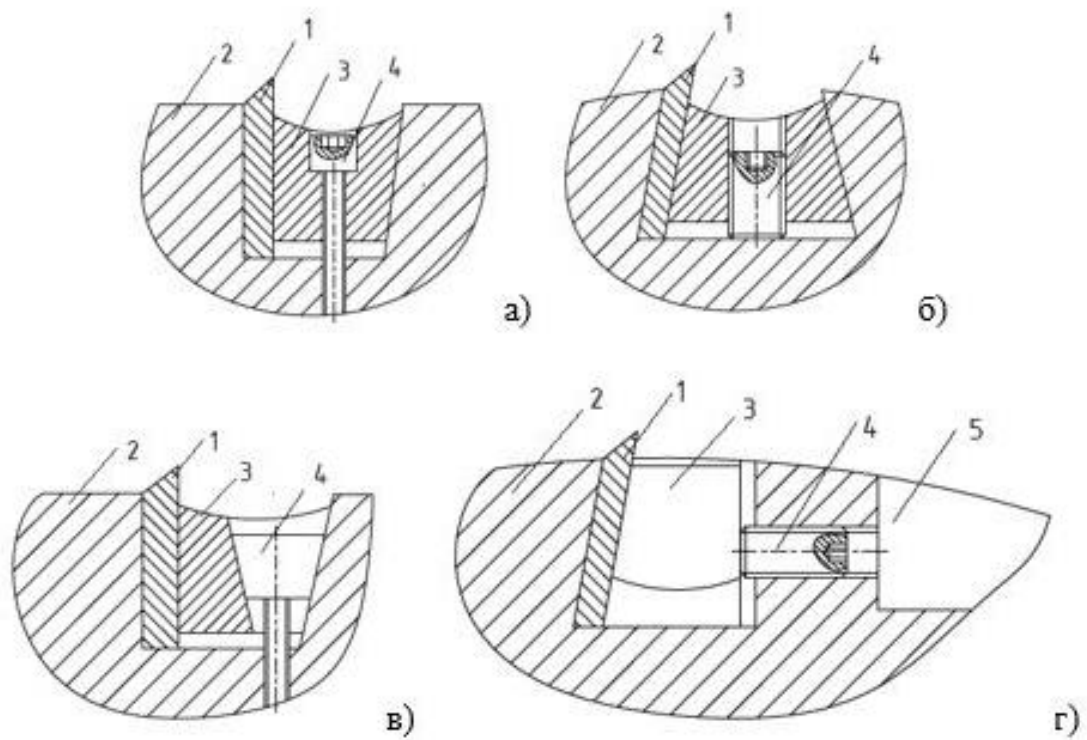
Види закріплення клином: а) диференціальний клин, б) гвинт без шапки, в) «половинчастий» г) боковий; 1-пластина, 2-корпус фрези, 3- клин, 4- гвинт, 5- канавка для гвинта[8]
